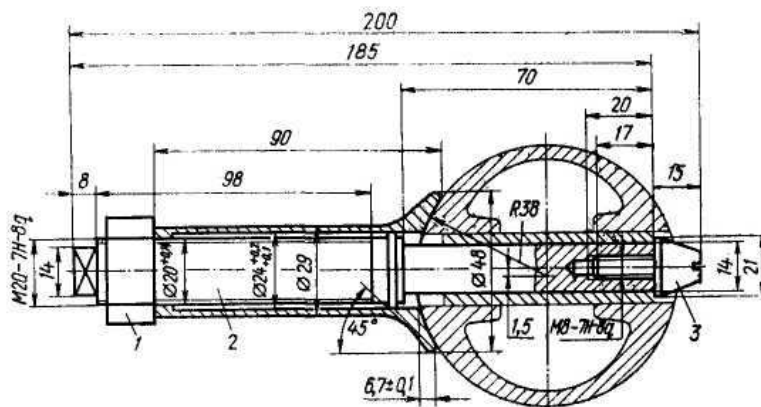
Приспособление для выпрессовки поршневого пальца:
